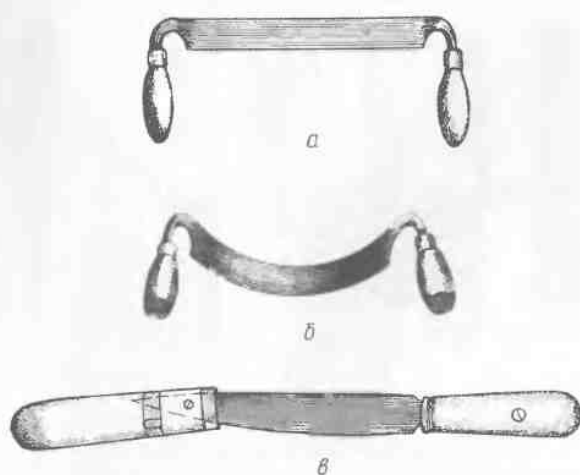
Инструменты для строгания древесины двумя руками: *а* — скобель прямой для снятия коры и стружки с бревен; *б* — скобель полукруглый для чернового строгания древесины и выборки полостей; *в* — приспособленный прямой скобель из ножа с приставной ручкой
